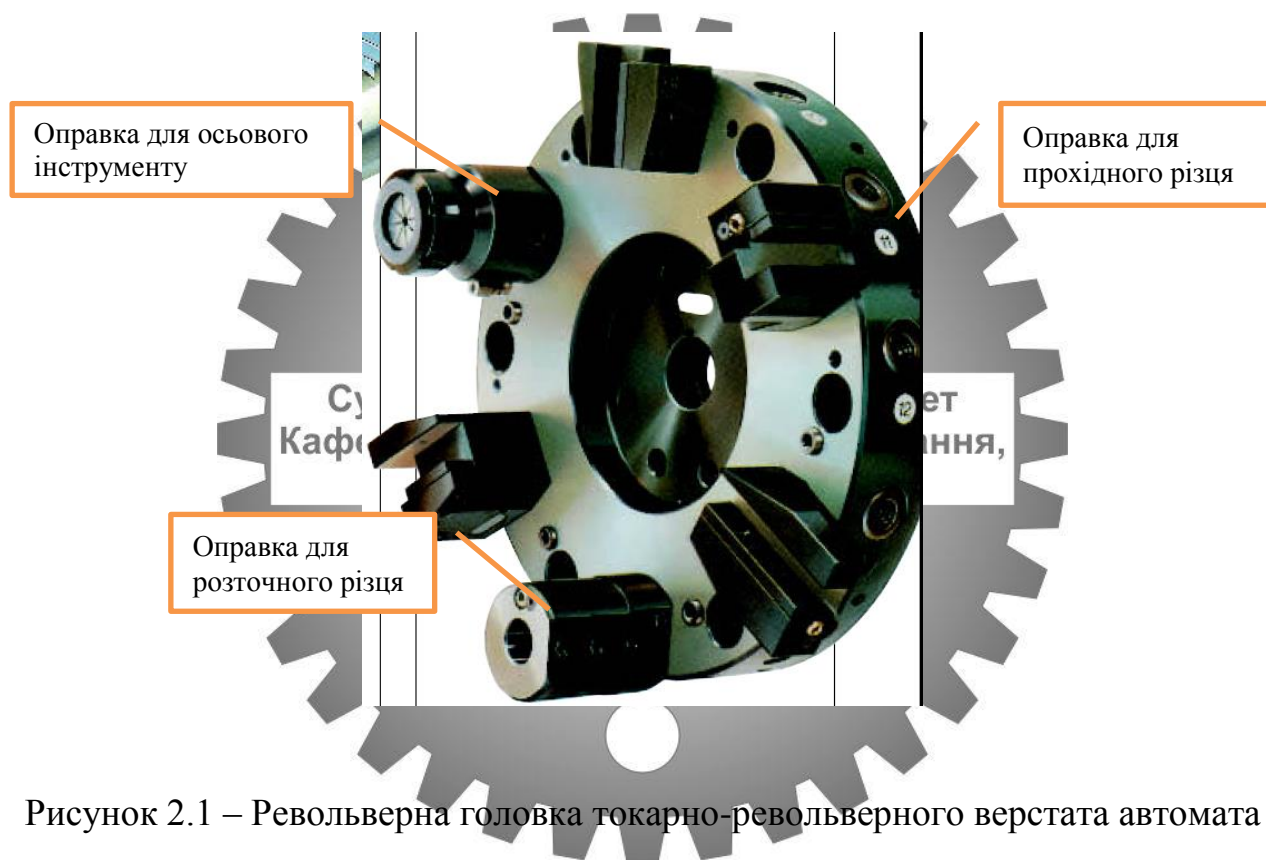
Револьверна головка токарно-револьверного верстата автомата
